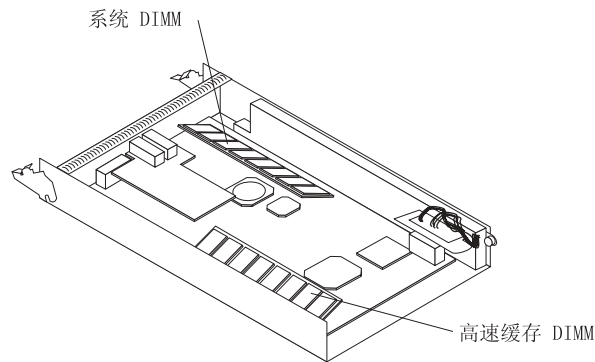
高速缓存 DIMM 和系统 DIMM 的位置
